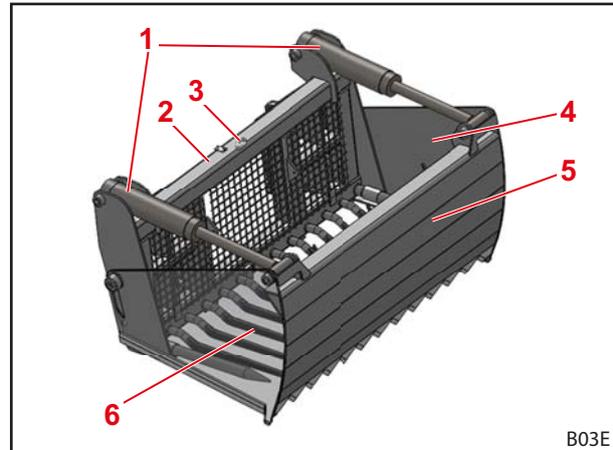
Struttura benna desilatrice con 2 cilindri idraulici
